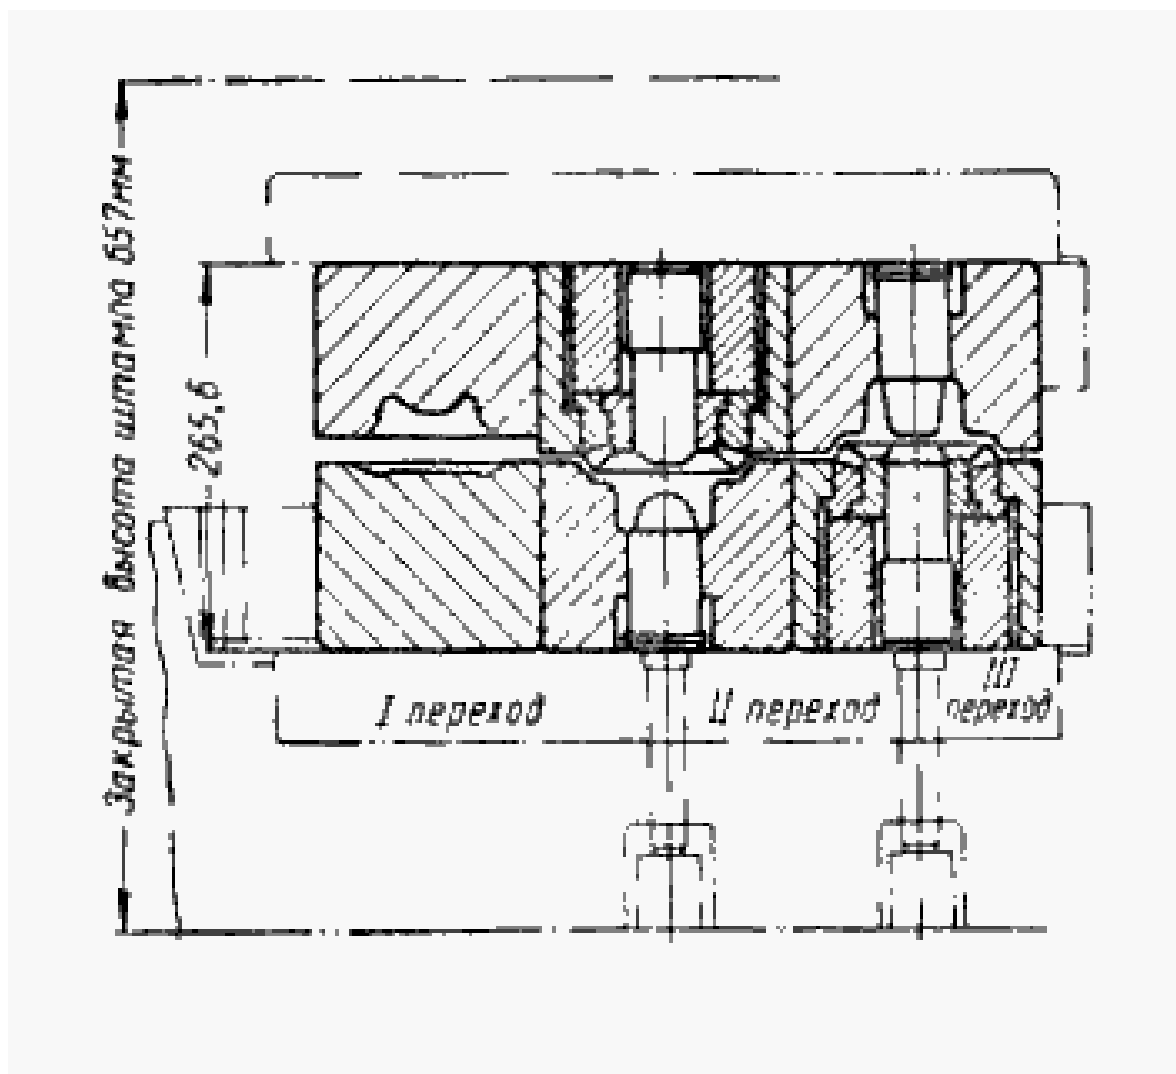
Схема штамповки шестерни с оформлением зубьев в предварительном и окончательном переходах
